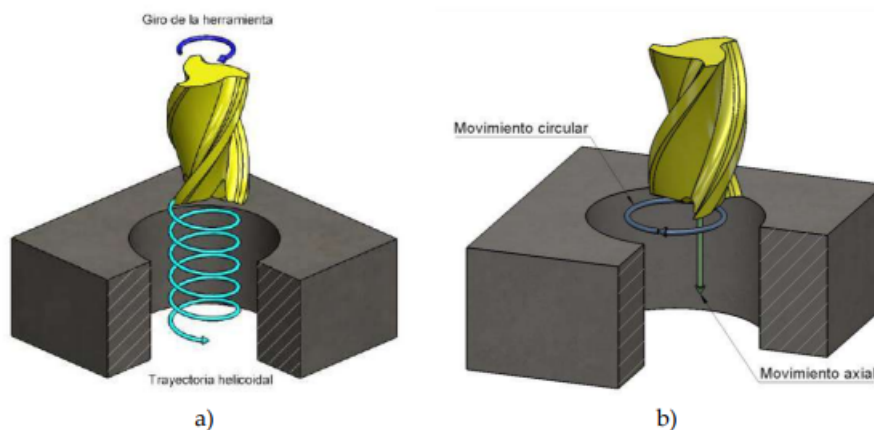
a) Movimiento de fresado helicoidal. b) Descomposición del movimiento helicoidal.
